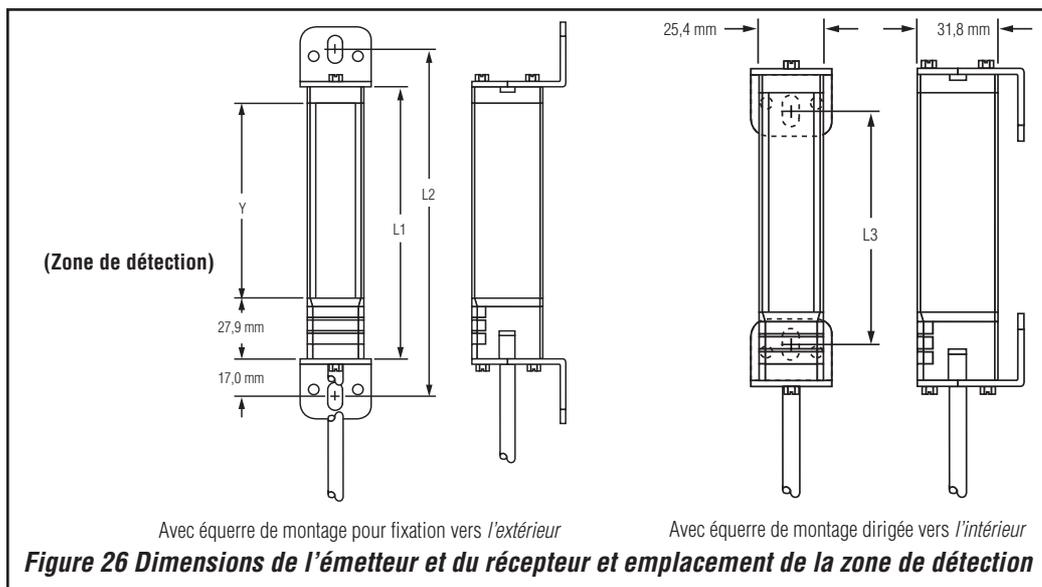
Dimensions de l'émetteur et du récepteur et emplacement de la zone de détection
